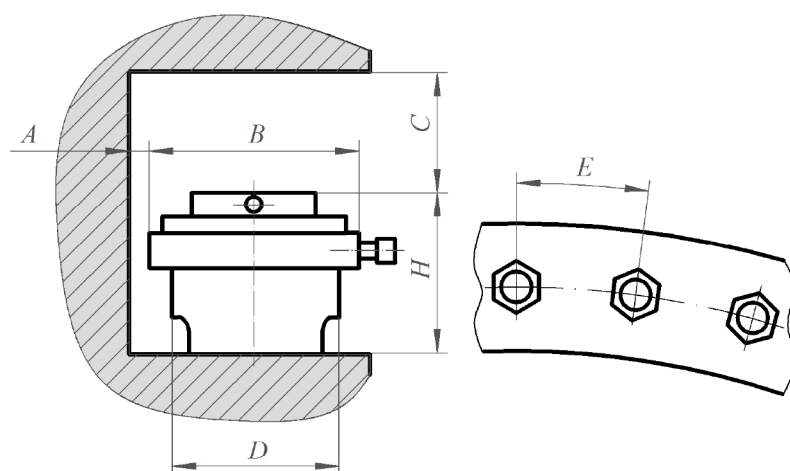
Схема к выбору размеров деталей для установки гидроключа для сборки резьбового соединения
